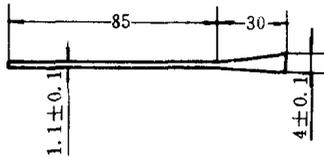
喷气嘴上开口 (尺寸单位: mm)
